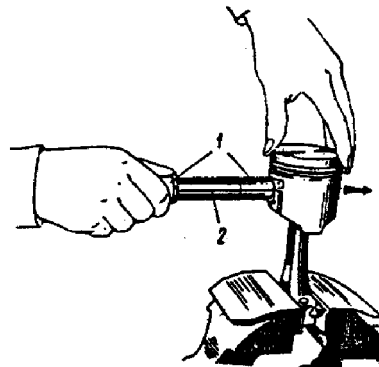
Instalação do pino do êmbolo: 1 - dispositivo 02.7853.9500; 2 - pino do êmbolo.
